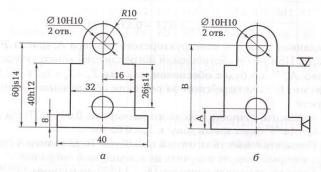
Чертеж детали (а) и схема базирования заготовки (б)
